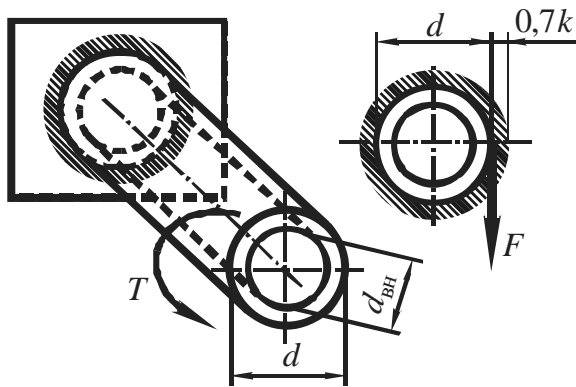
Схема углового сварного шва (тавровое соединение), нагруженного крутящим моментом
